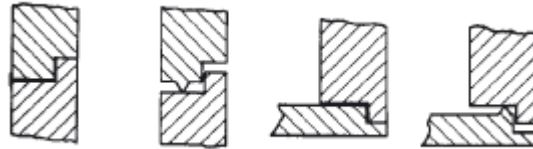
Stumpfschweißnaht Varianten [13]
